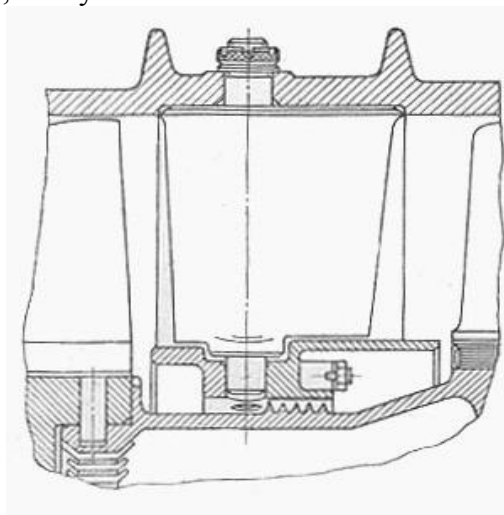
Неразъемное крепление направляющих лопаток точечной сваркой.
